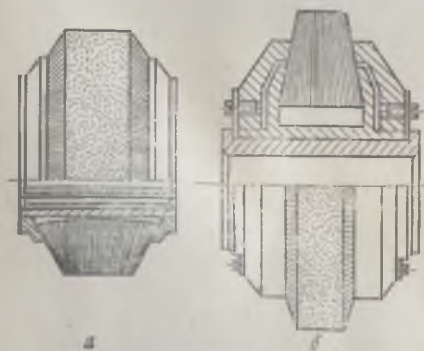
Иглофрезы: а — бескорпусная; б — корпусная.
